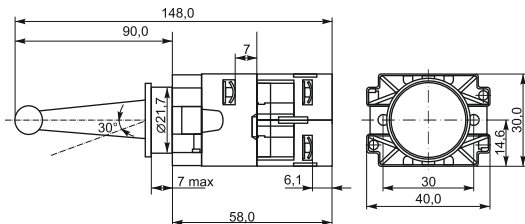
Габаритные и установочные размеры изделий для цепей управления
